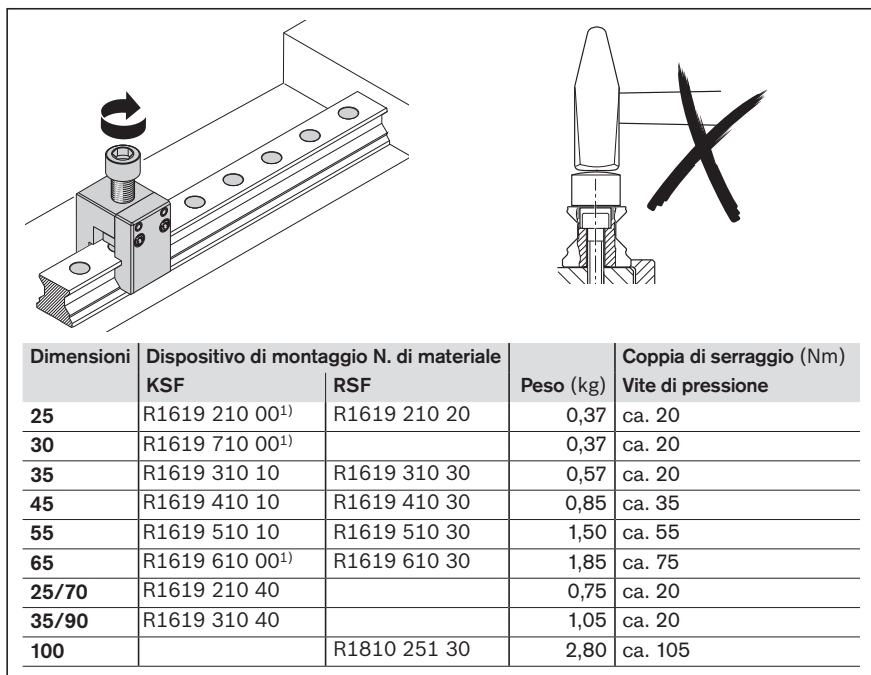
Dispositivo di montaggio per tappi di chiusura fori
